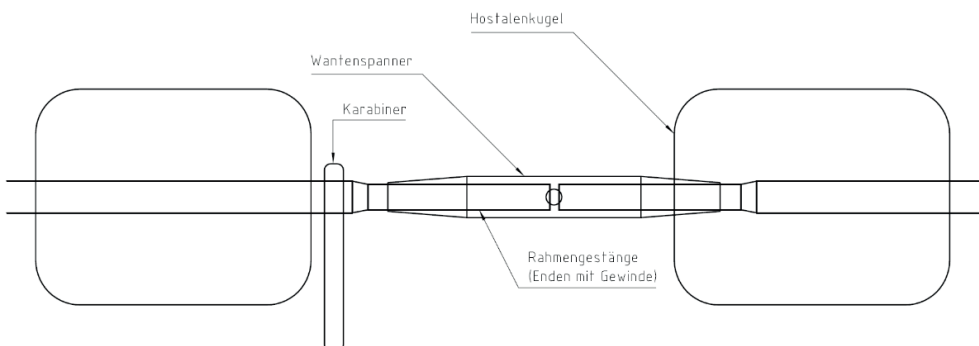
Detailansicht des Wantenspanners – verschraubt
